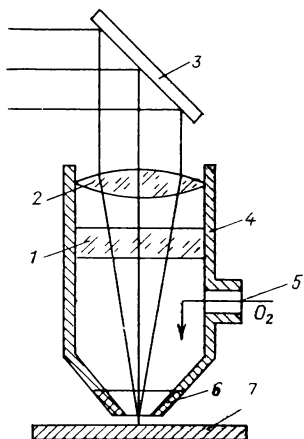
Оптический резак. 1 — защитная пластина; 2 — фокусирующая система; 3 — отклоняющее зеркало; 4 — корпус; 5 — штуцер для ввода сужающего газа; 6 — сопло; 7 — обрабатываемый лист.
